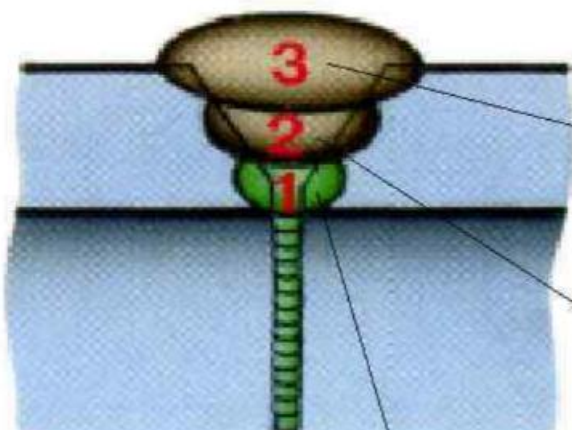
Структура швів зварювання: 1 – облицювальний шар зварного шва; 2 – заповнюючий шар зварного шва; 3 – корінь зварного шва
